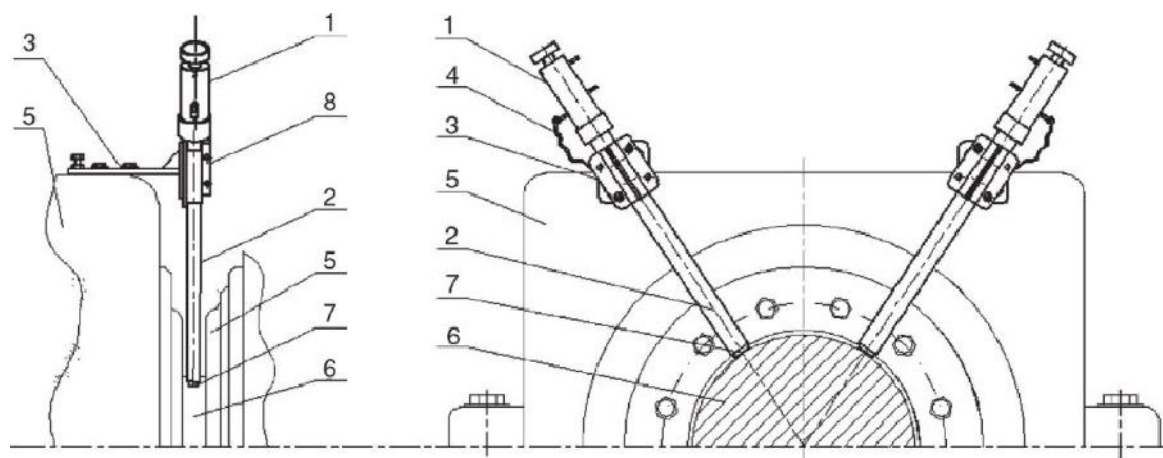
Схема установки заземляющего токосъемного устройства К10-1 на корпус подшипника турбины: 1 – блок настройки и индикации; 2 – направляющая; 3 – кронштейн; 4 – кабель соединительный; 5 – корпус турбины (машины); 6 – вал; 7 – электрографитная щетка; 8 – хомут
